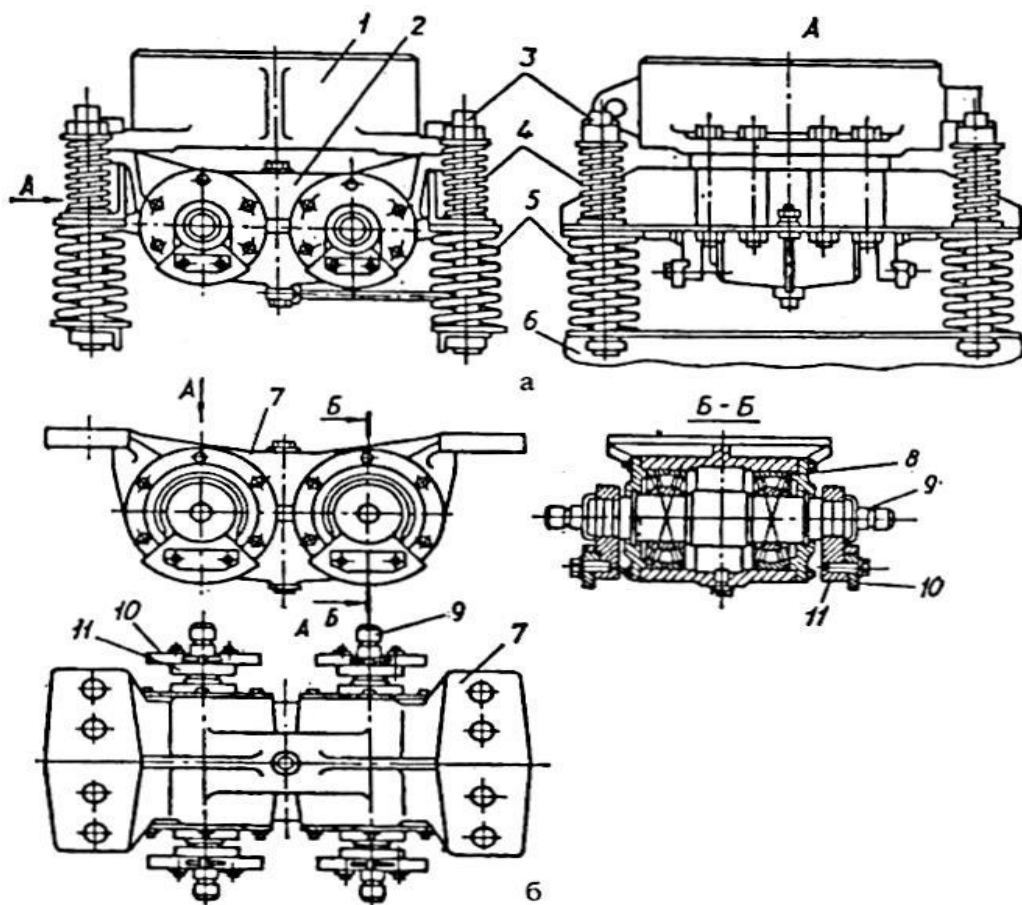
Вібраційний блок: а — загальний вигляд; б — вібробудувач.
